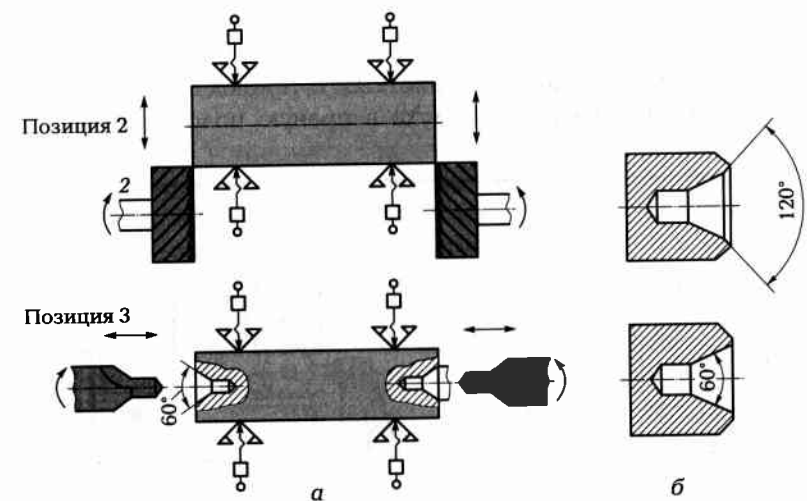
Схема наладки фрезерно-центровального полуавтомата для обработки вала (а) и конструкция центровых отверстий (б)
